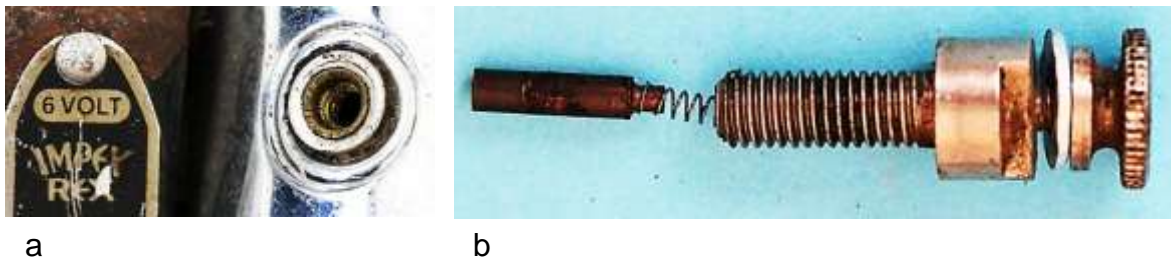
Spannung führender Kontakt: a) Gewindeeinsatz im Gehäusemantel, b) Kombination aus Bürstenhalter und Kabelanschlussbolzen mit Bürste
